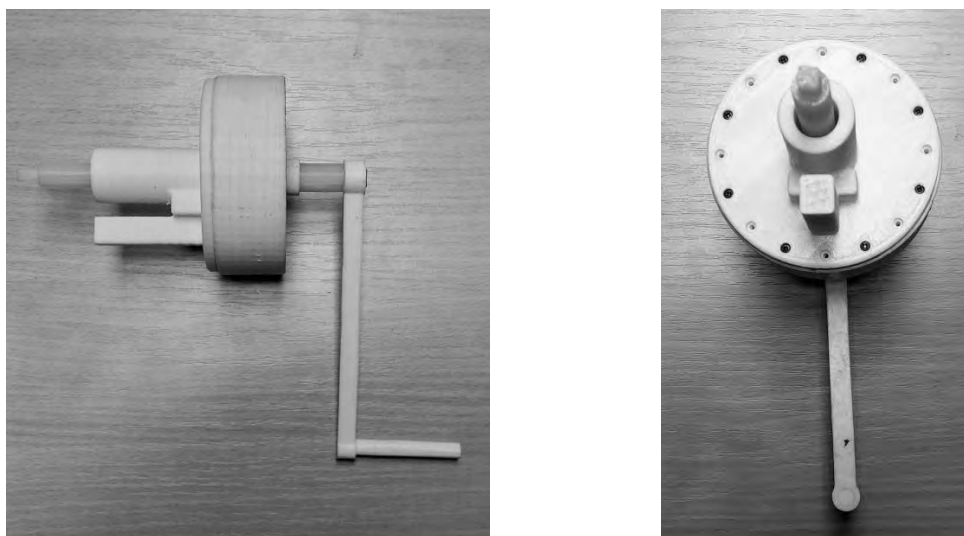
Общий вид 3D-модели гайковерта с усилителем
